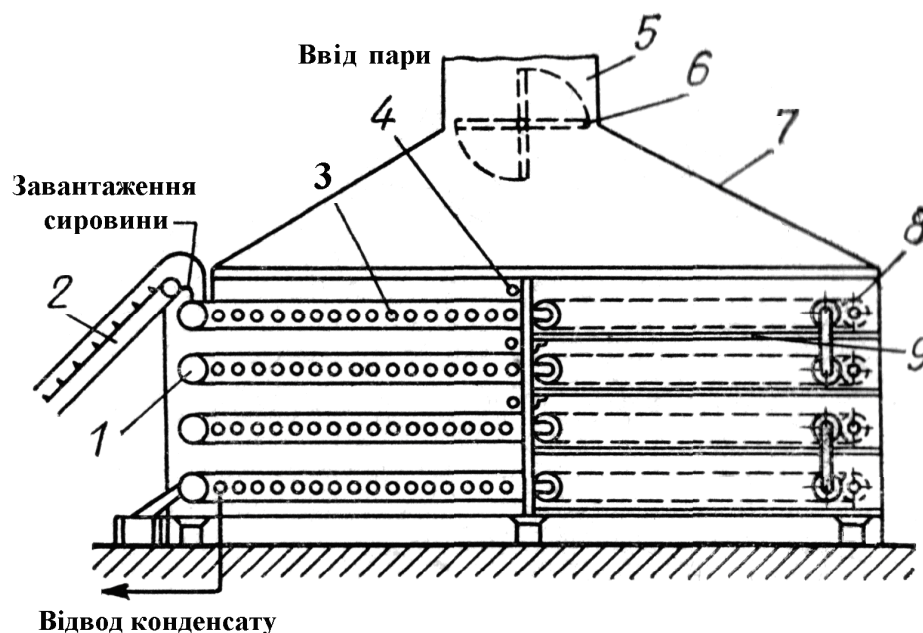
Конвеєрна чотиристрічкова сушарка: 1 – ведучий барабан; 2 – похилий транспортер; 3 – калорифер; 4 – перегрівач; 5 – витяжна труба; 6 – шибер; 7 – витяжний ковпак; 8 – натяжний барабан; 9 – стрічкоочищувач
